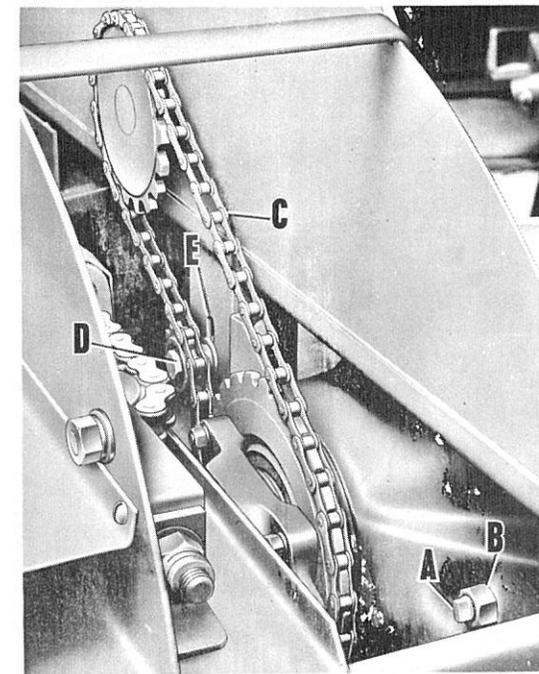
Réglage de la butée arrière et de la chaîne d'entraînement principale.
